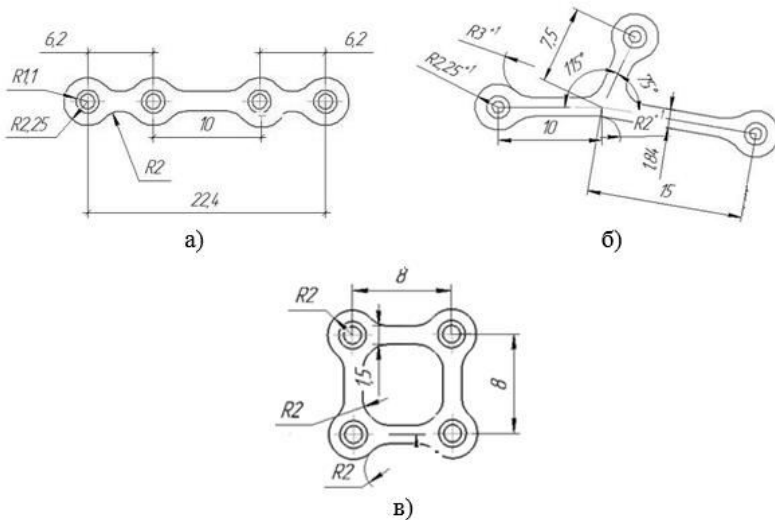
Конструкція та розміри пластин: а – пряма; б – Y – пластина; в – пластина-квадрат
